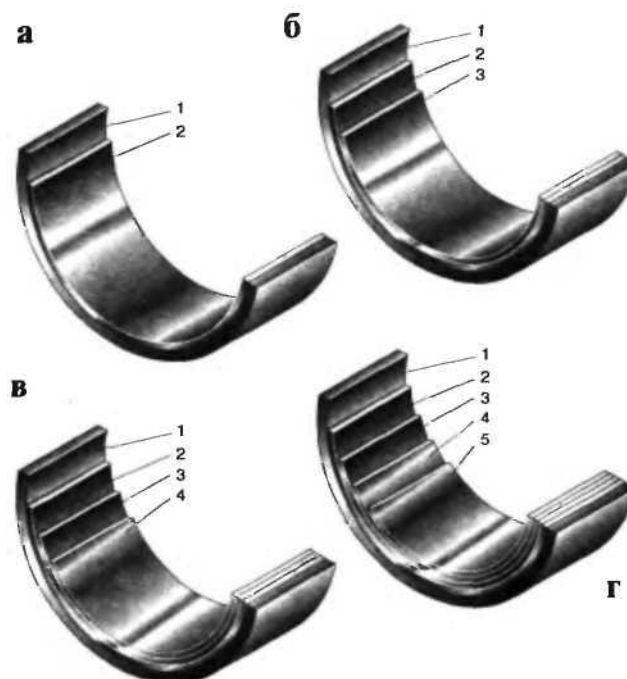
Класична будова типових підшипників ковзання: а - 2-спойные; б - 3-слойные; в - 4-слойные; г - 5-слойные; 1 - сталевая основа; 2 - основной материал; 3 - підшар; 4 - основне покриття; 5 - додаткове покриття (олово)
